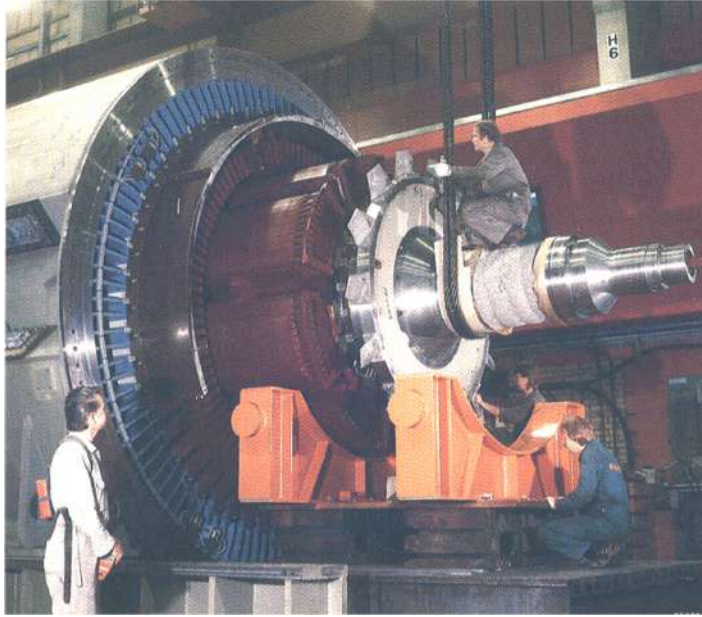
rotor d'une machine synchrone à pôles saillants.
